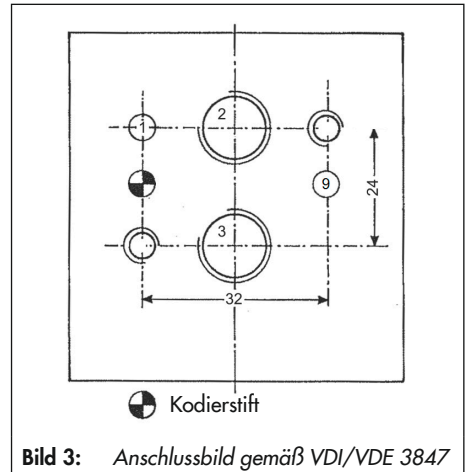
Anschlussbild gemäß VDI/VDE 3847
